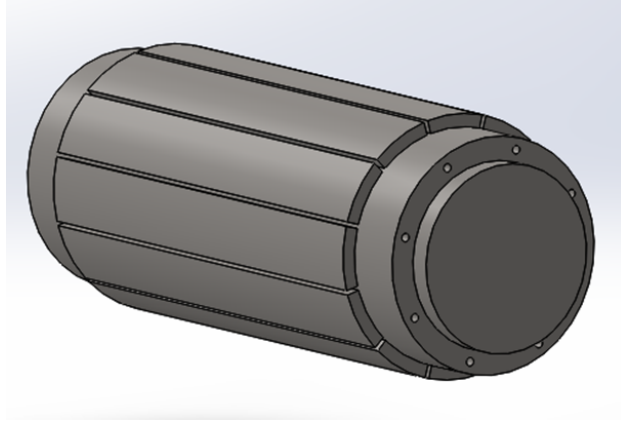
Tren epicicloidal de engranajes (Gearbox).
